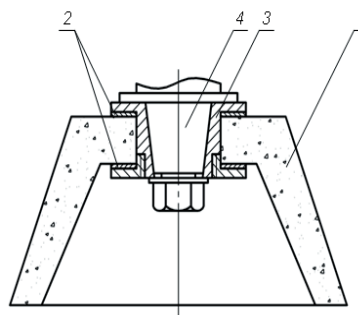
Схема установки шлифовального круга на сателлитный шпиндель
